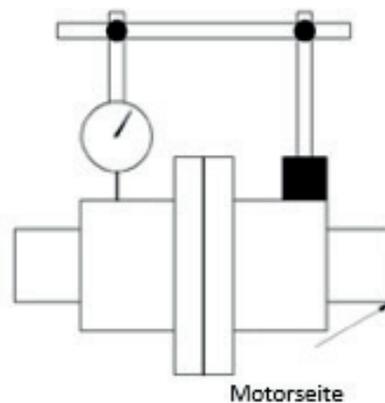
Ausrichtung der flanschmontierten Pumpe
